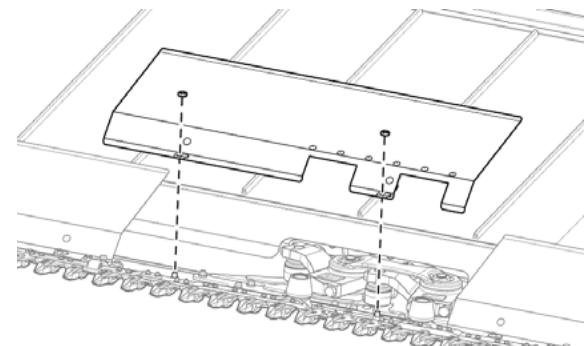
Снятие первевой пластины, расположенной над подшипниками ножей.
